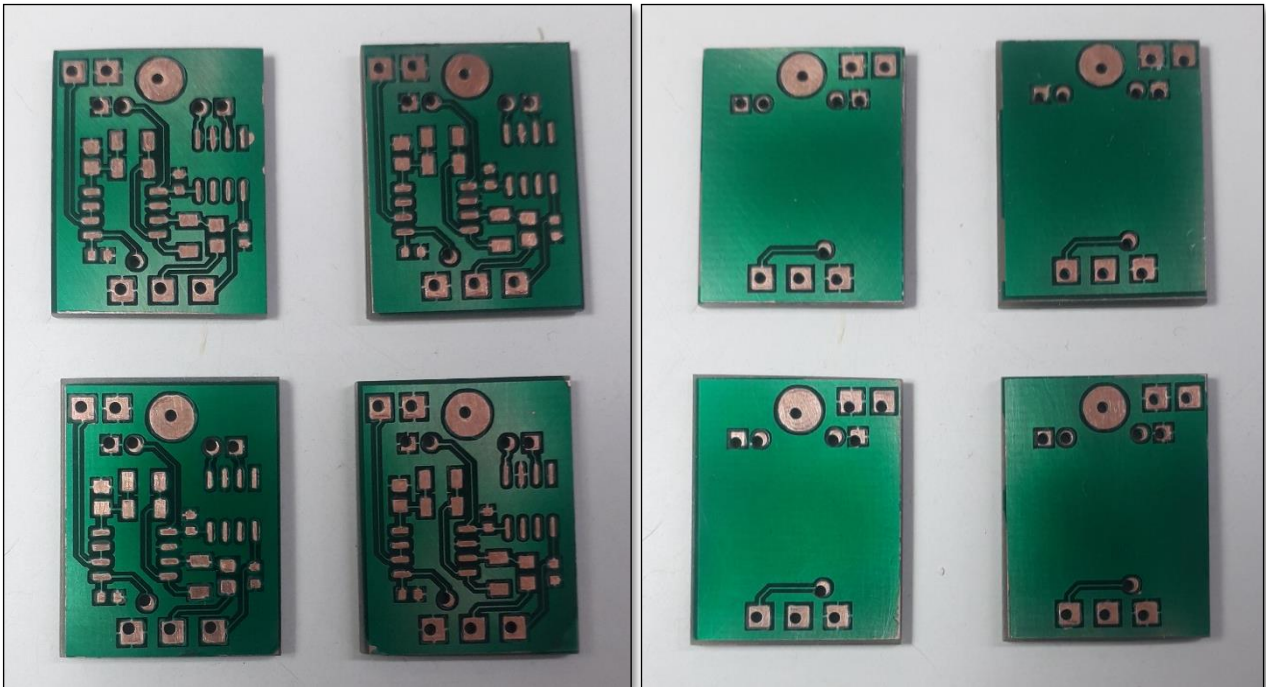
PCBs de Bobinas Rogowski sin componentes soldados
